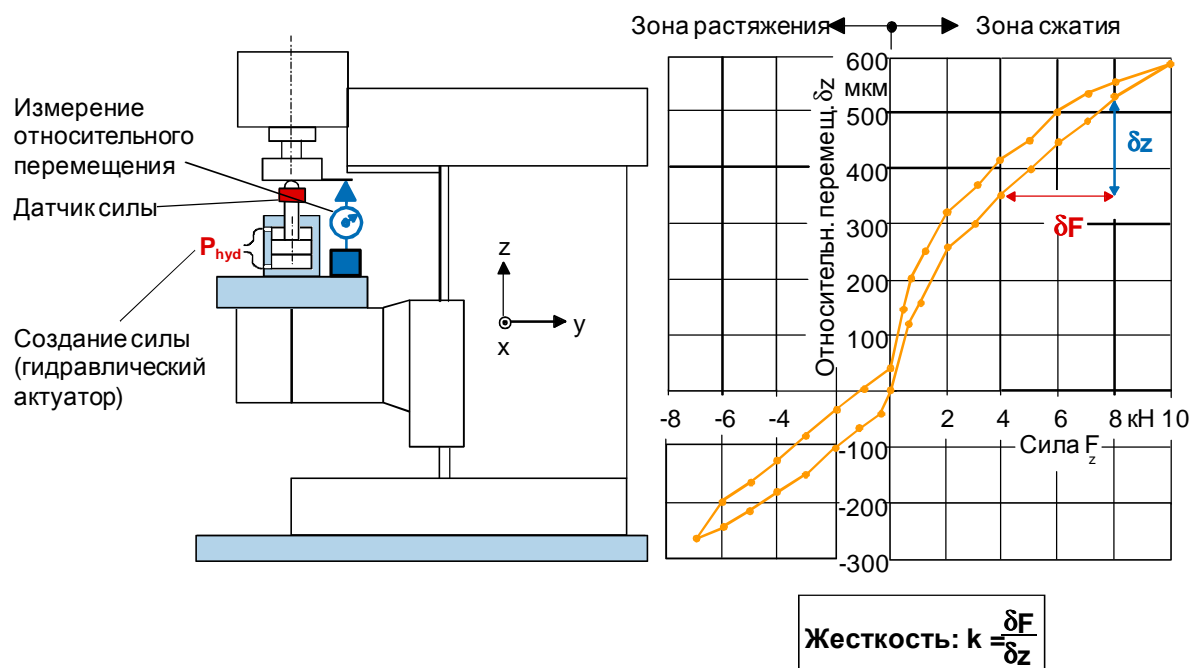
Определение статической жесткости в центре инструмента консольного вертикально-фрезерного станка
